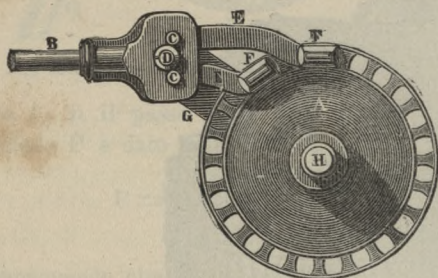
Veduta di fronte del meccanismo del torchio Mabille.
